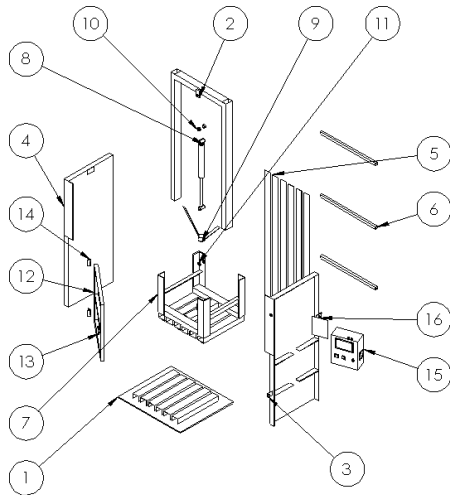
Vista explosionada de ensamble planta piloto de compactación.
